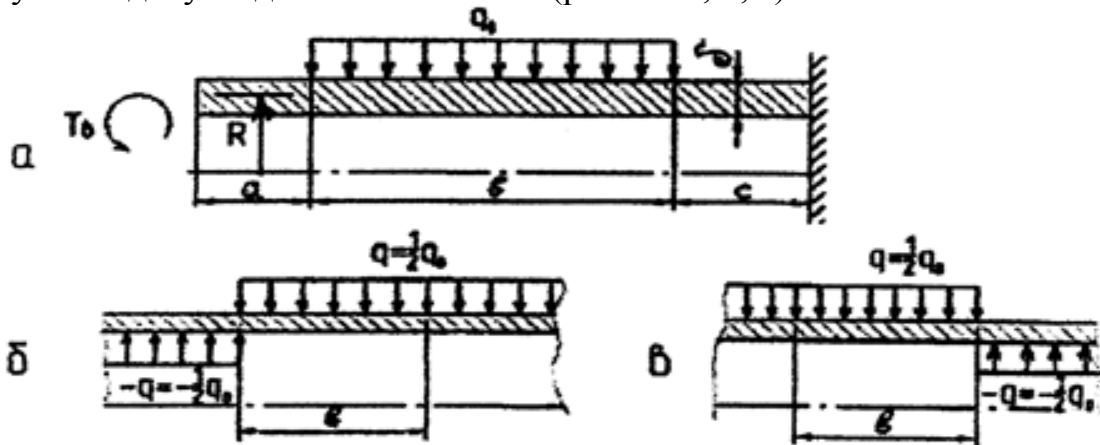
Розрахункова схема вала ЗЗЖ
